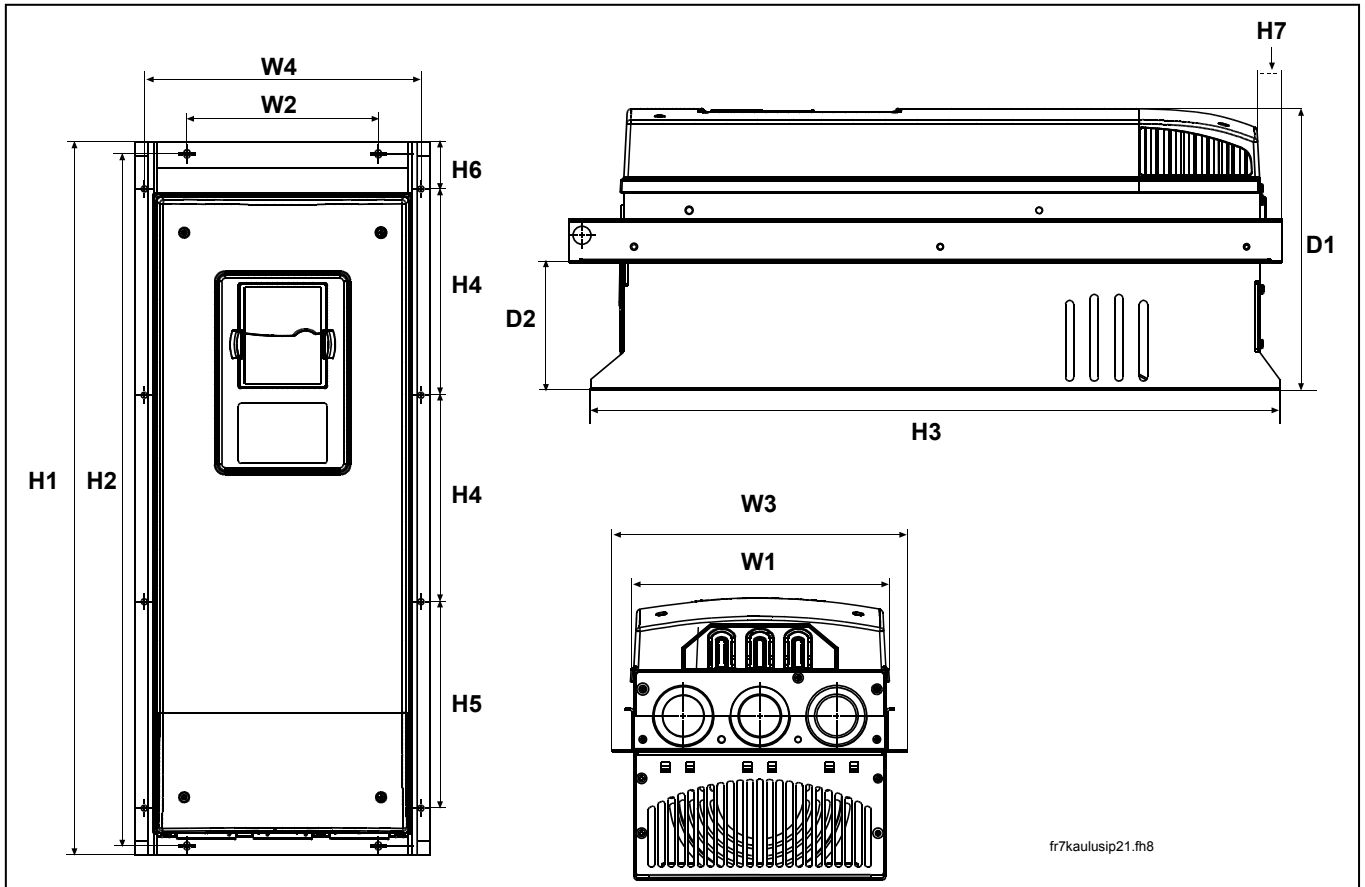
Габариты инвертора Vacon NX, IP21, с фланцем, FR4 и FR6
